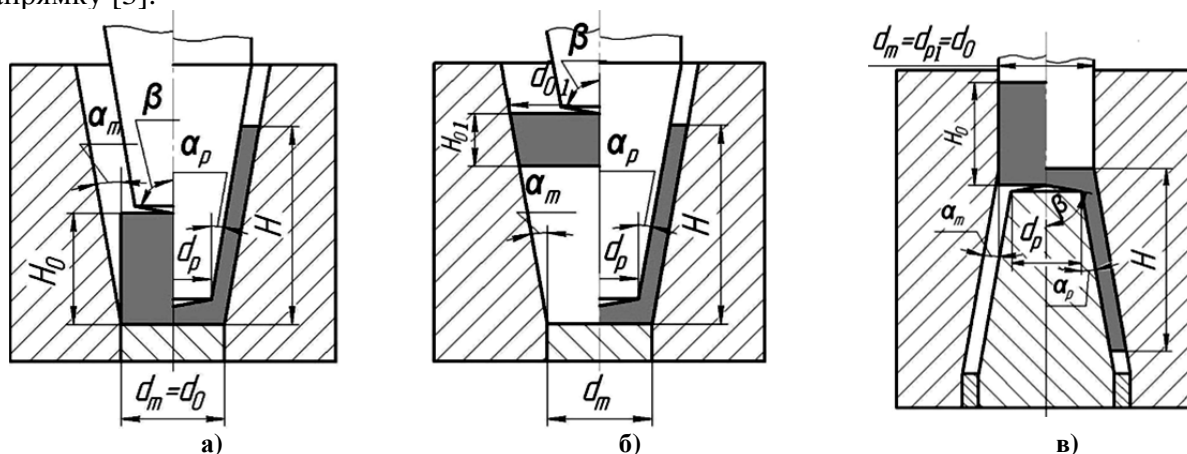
Схеми видавлювання порожнистої конічної деталі: а) зворотнє; б) комбіноване; в) пряме з роздачею.
